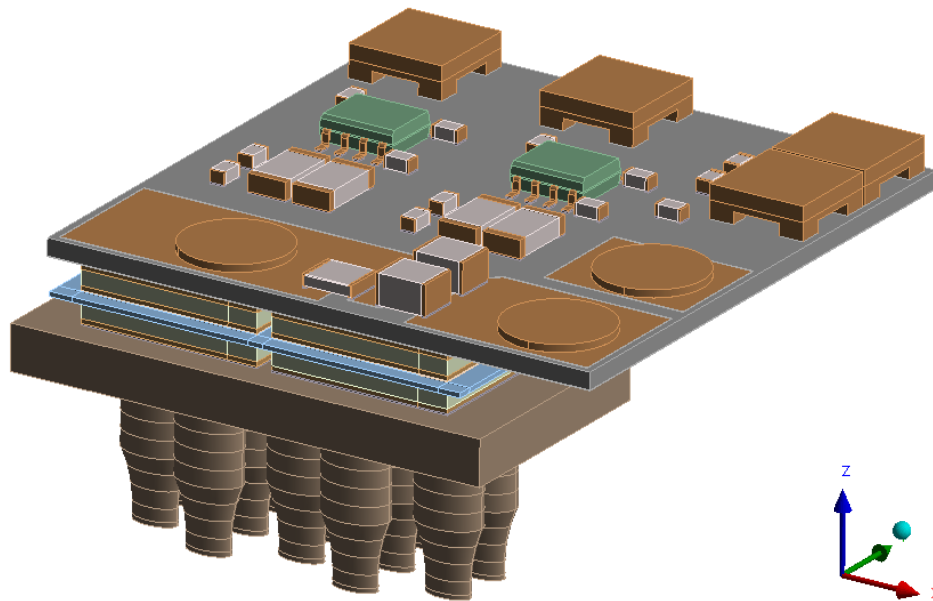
Finale vereinfachte CAD Geometrie des SiCool Demonstrators für den digitalen Zwilling.
